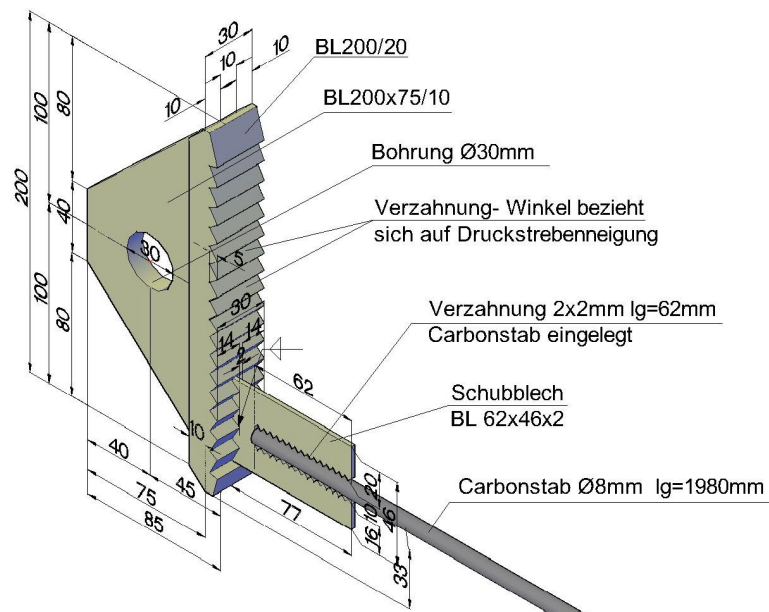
Stahlimplantatyp 2 mit CFK-Stab - Isometrieansicht
